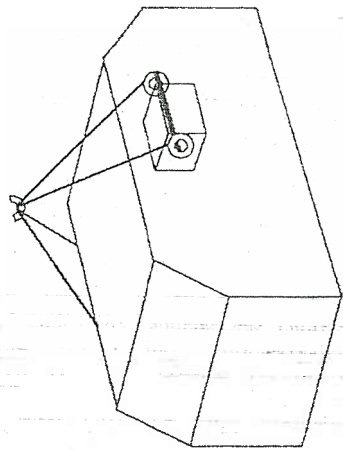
Схема строповки ящика с рым-цапфами в верхней части
